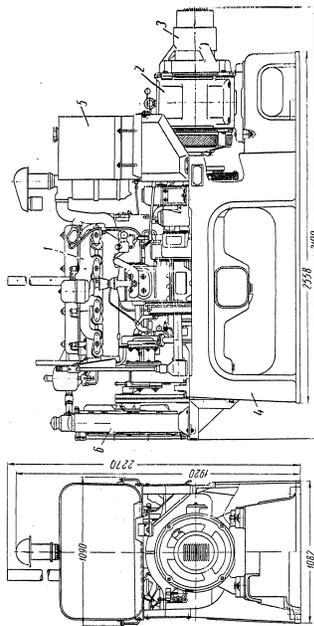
Общий вид станции с габаритными и установочными размерами: 1 — двигатель КДМ-46; 2 — силовой генератор СГ-60/6; 4 — рама; 5 — топливный бак; 6 — радиатор.
